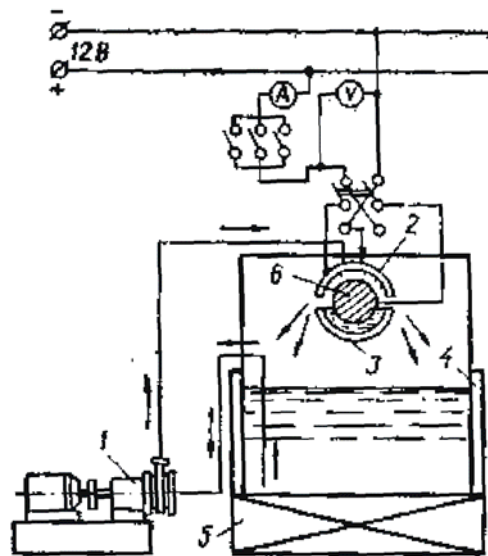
Схема установки для електролітичного покриття шийок вала:
